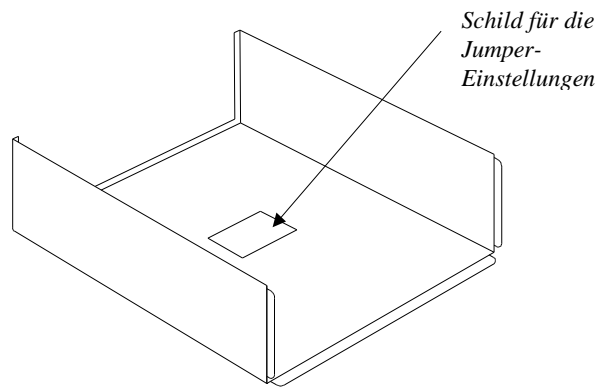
Lage des Schildes für die Jumper - Einstellungen
